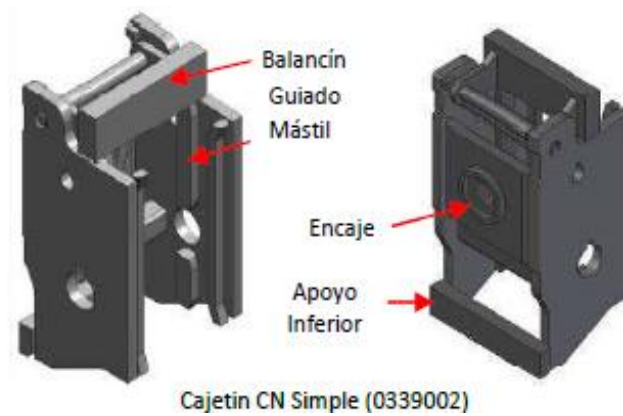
Detalle del cajetín simple utilizado para la fijación y soporte del sistema ATR. Recuperado de: Ulma Construction, *Consolas autotrepantes*.
